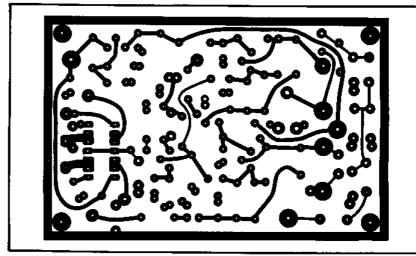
Circutt imprimé (éch. 1, double face, I face vierge) du générateur de porteuse.
